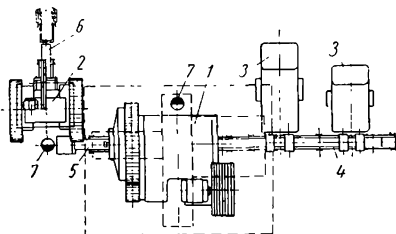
Схема расположения пластинчатых транспортеров в агрегате кривошипного горячештамповочного пресса: 1 — кривошипный горячештамповочный пресс; 2 — обрезной пресс; 3 — индукционные нагреватели; 4—6 — пластинчатые транспортеры; 7 — рабочие места
